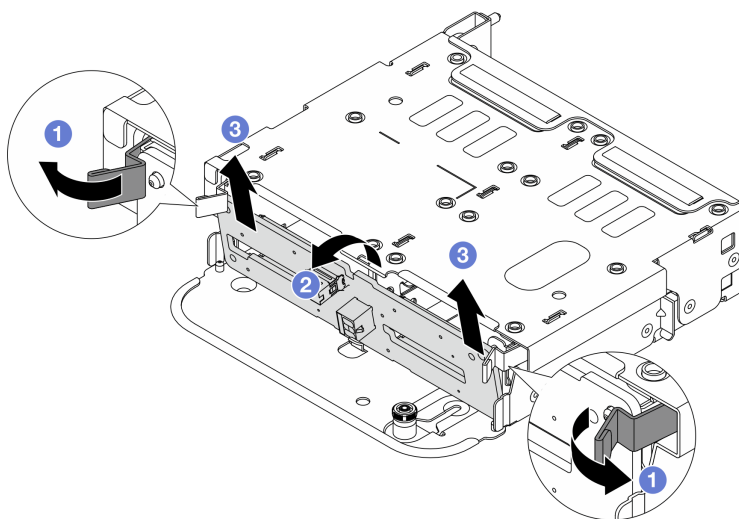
Entfernen der hinteren Rückwandplatine für 4 x 2,5-Zoll-Laufwerke
